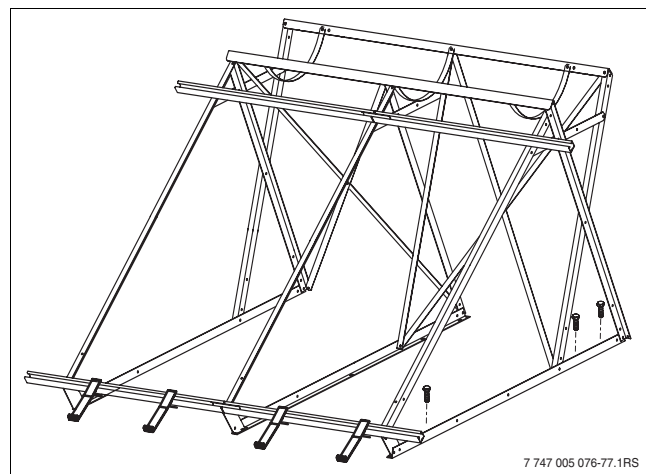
Instalación en el tejado sistema para cubierta plana (aquí sistema de 300 l)
